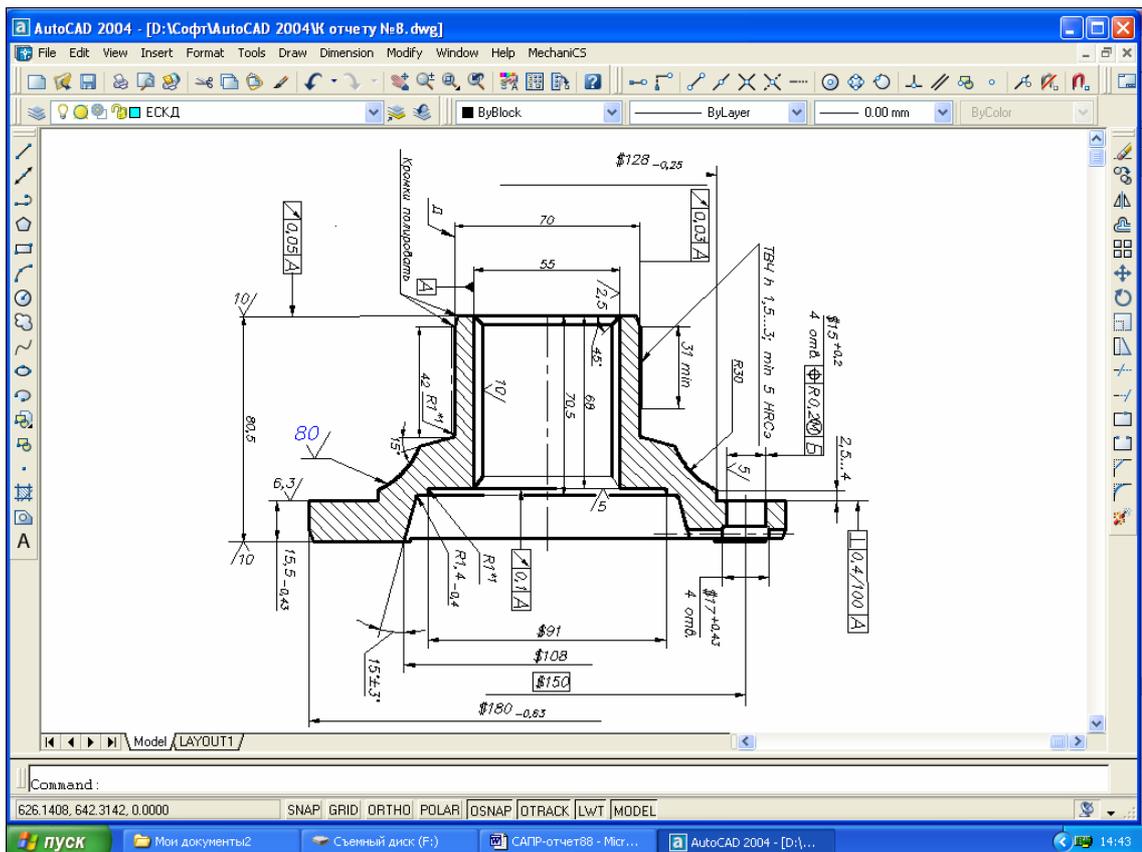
Чертеж детали «фланец» в AutoCAD
